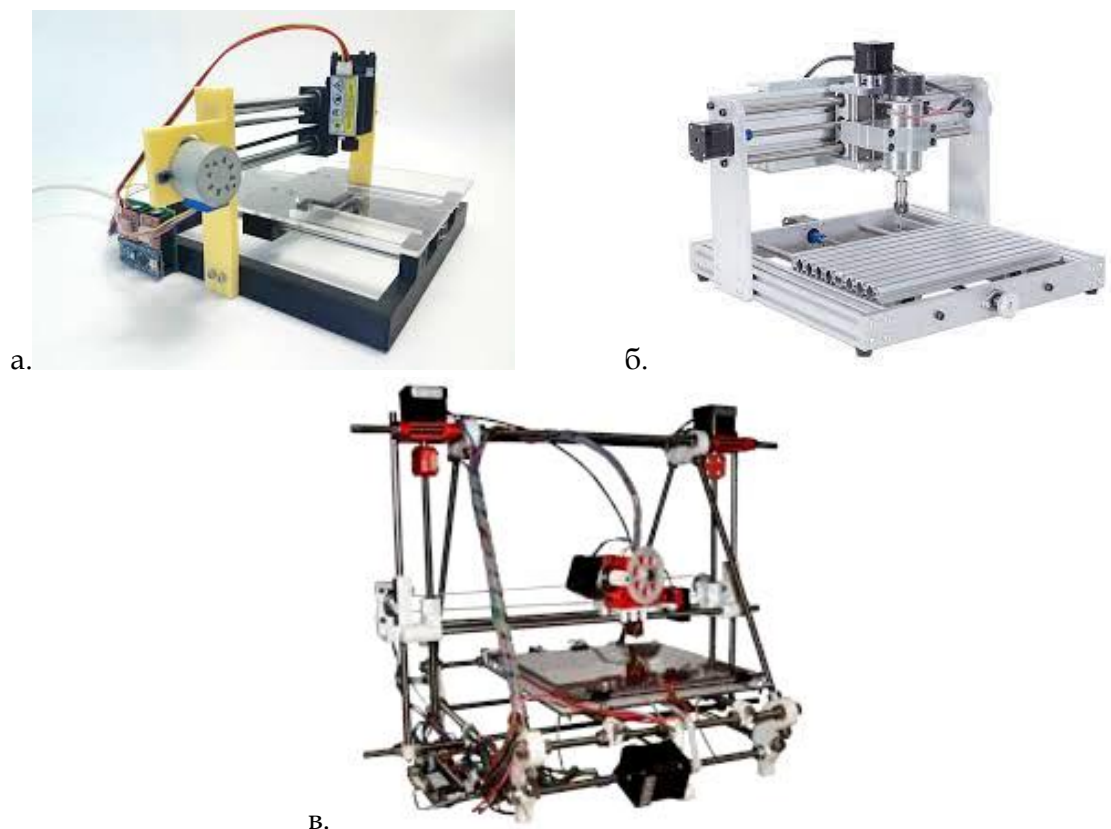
Конструкції саморобних верстатів з ЧПУ (а. лазерний випалювач, б. ЧПУ фрезер, в. 3D принтер)
